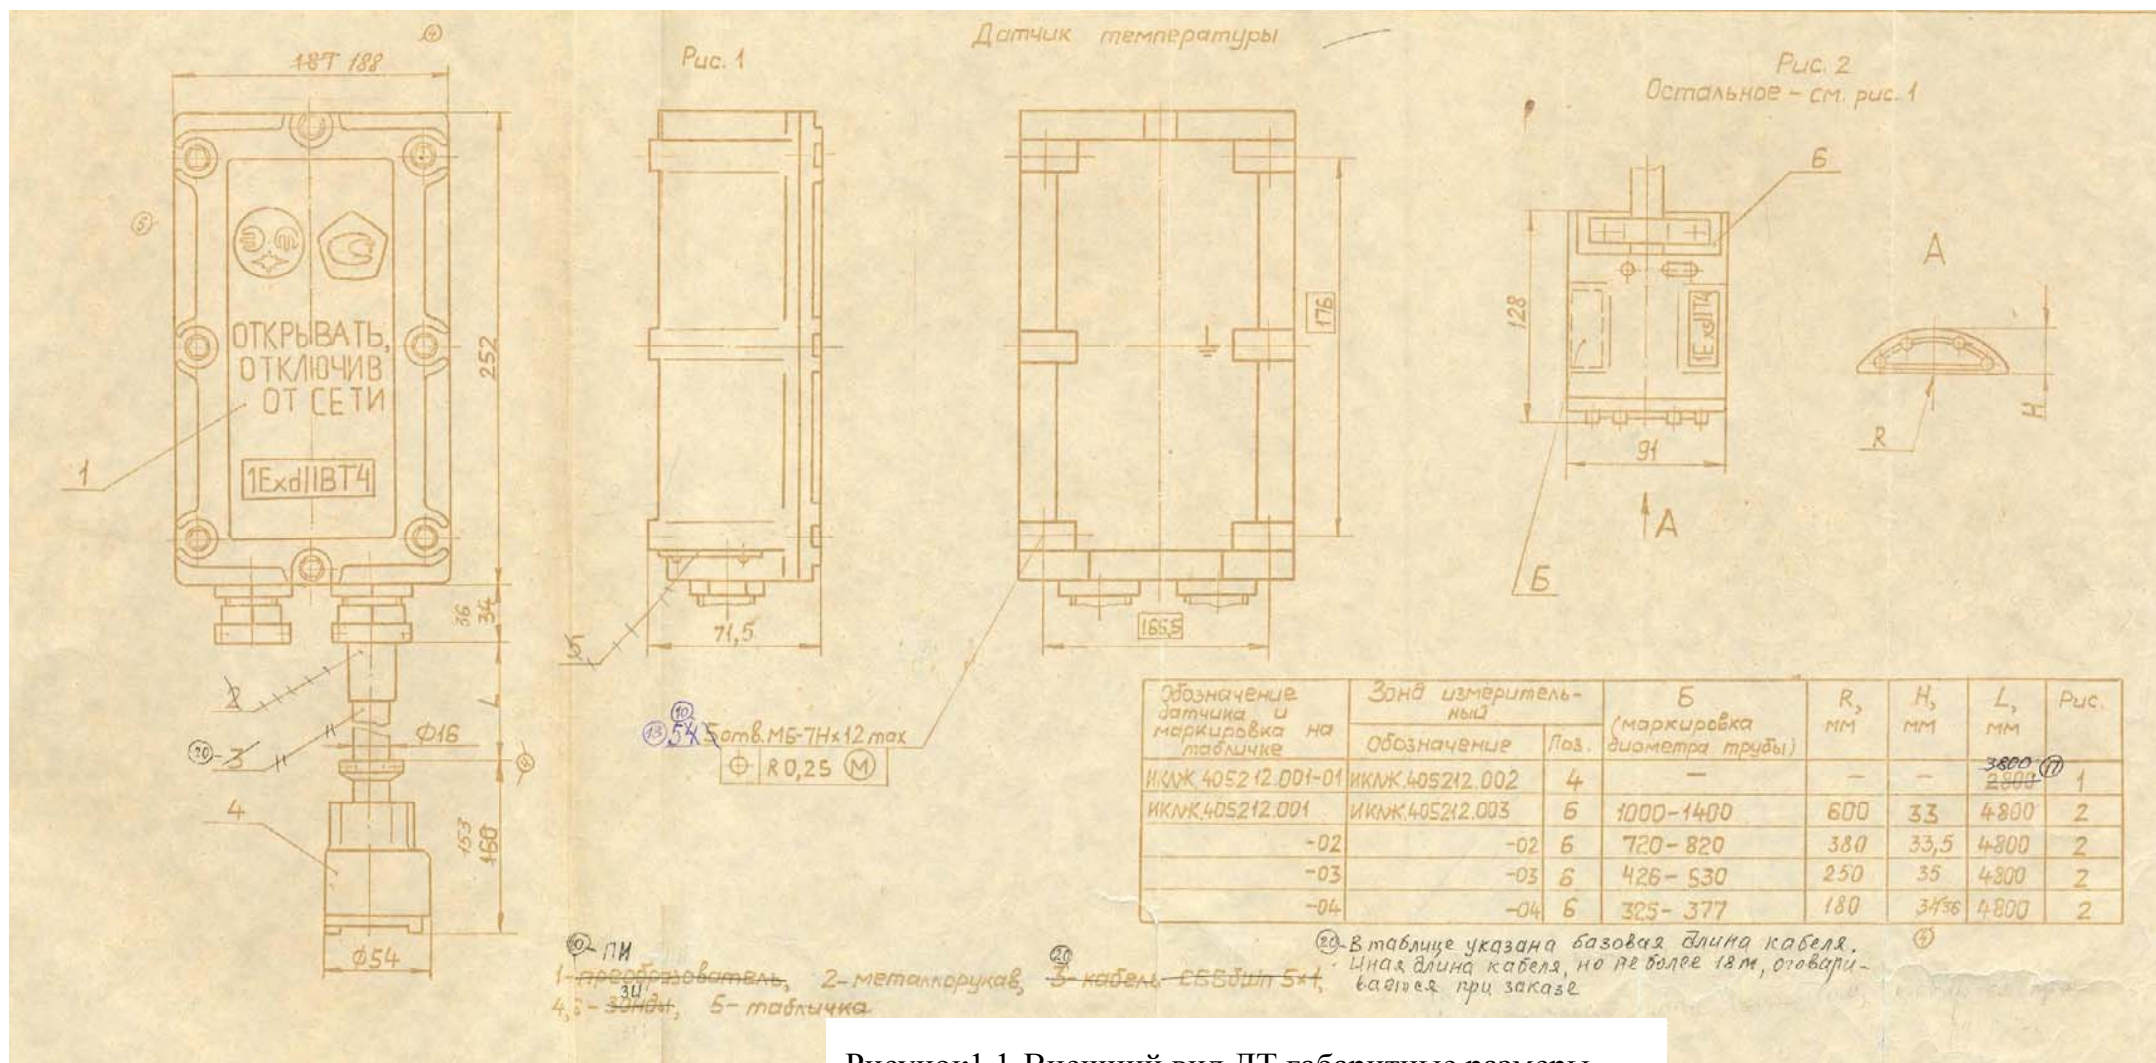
Внешний вид ДТ, габаритные размеры
